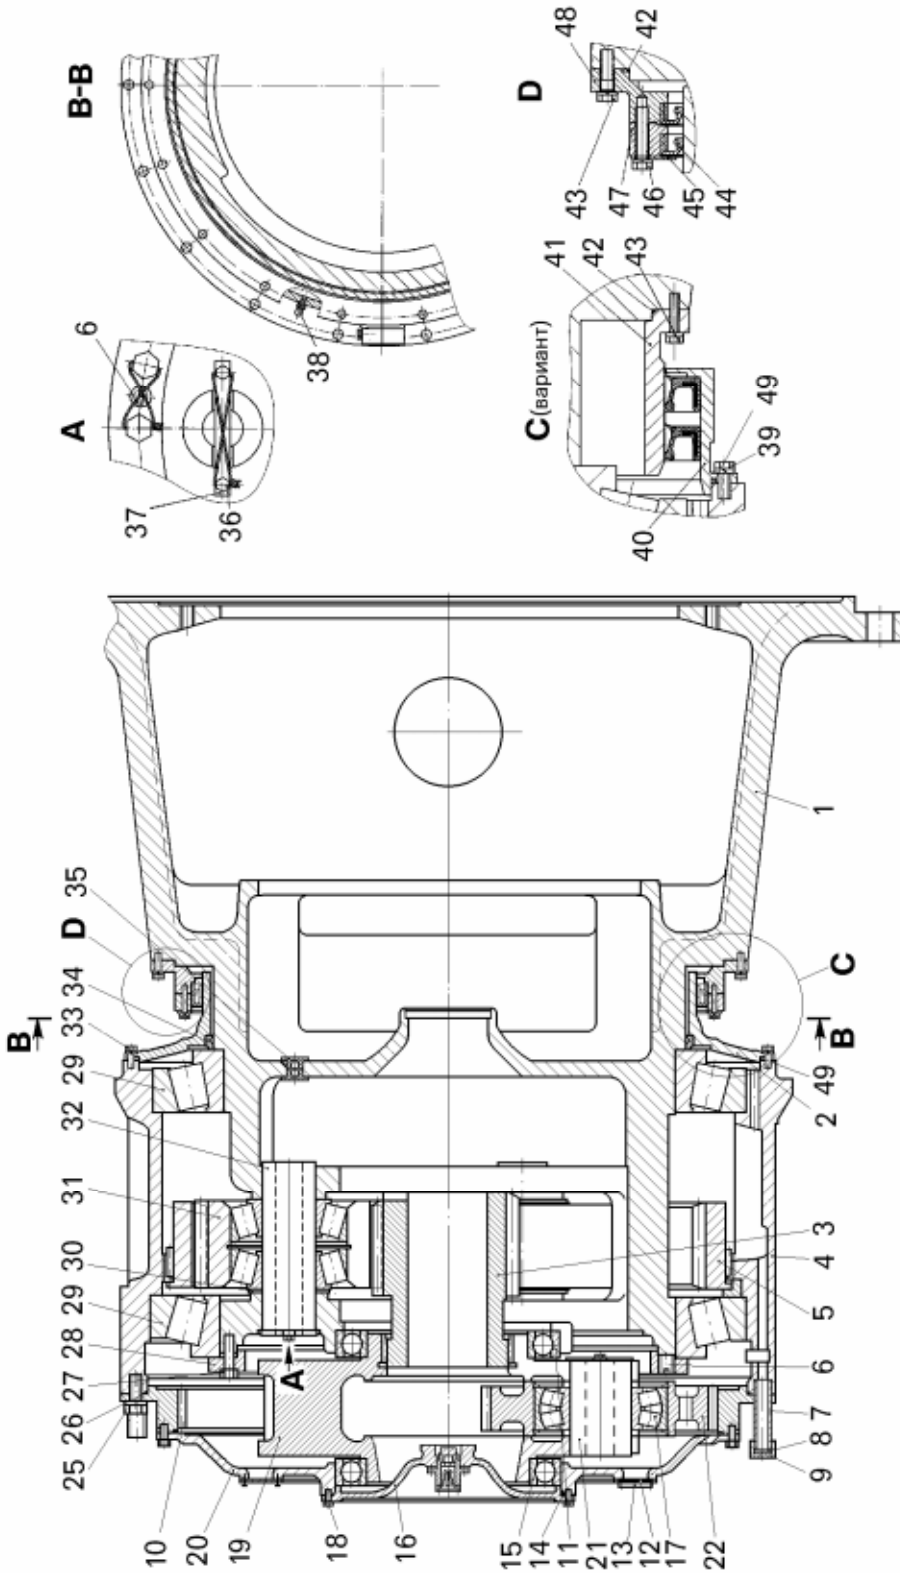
Редуктор мотор-колеса 7520:
